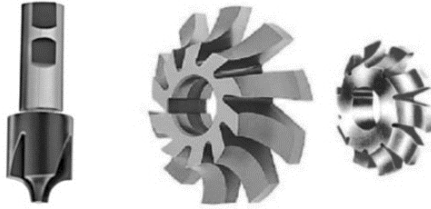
ดอกกัดด้านข้าง Side Milling Cutter
